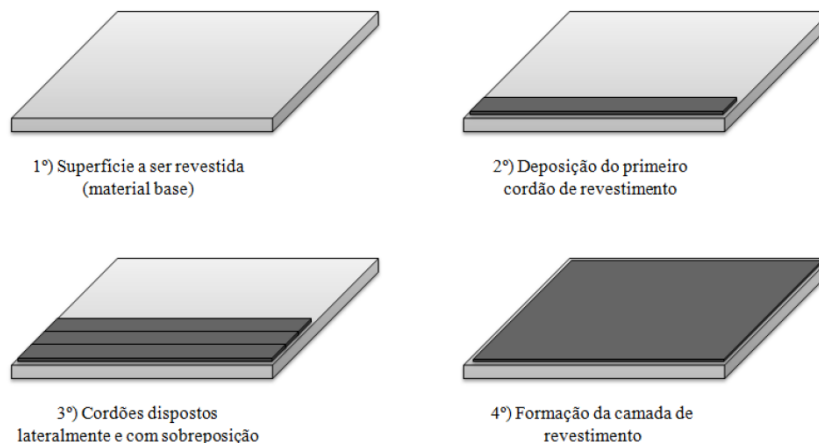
Etapas do processo de soldagem de revestimento (GOMES, 2010)
